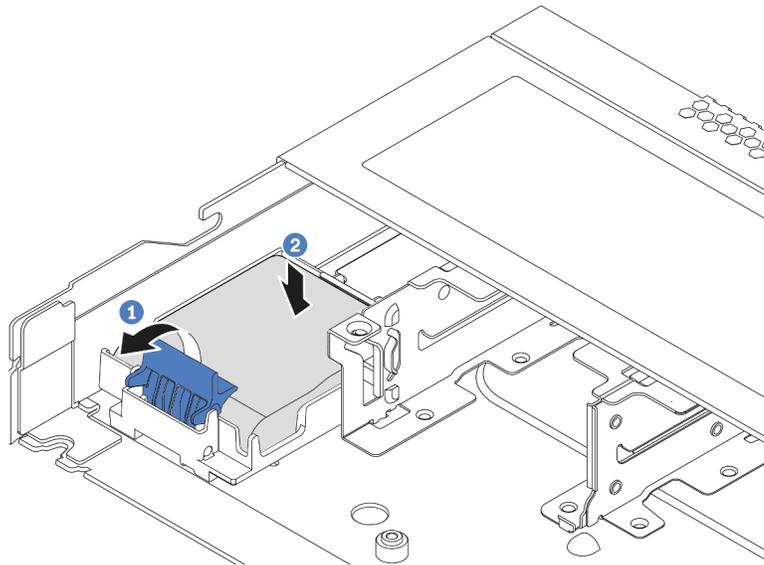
Installazione del modulo di alimentazione flash RAID sullo chassis
